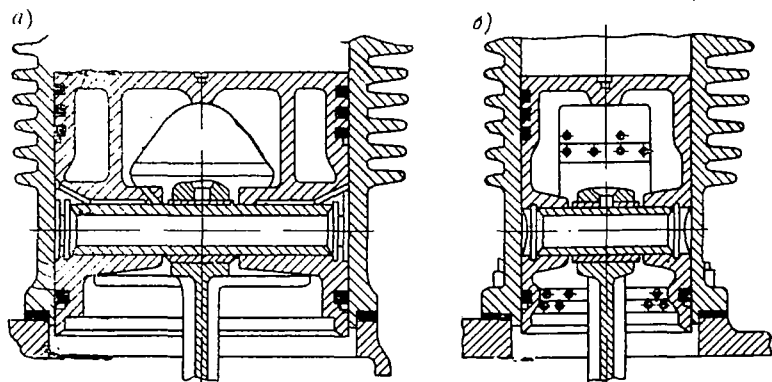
Шатунно-поршневая группа I и II ступени компрессора ЗИФ в сборе
